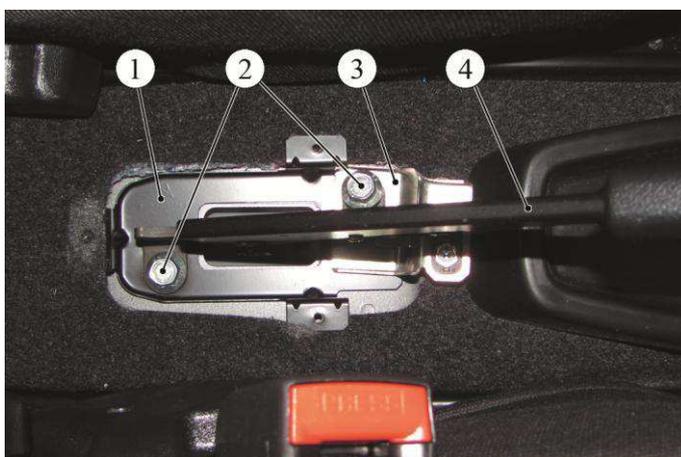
Снятие рычага ручного привода тормоза:
